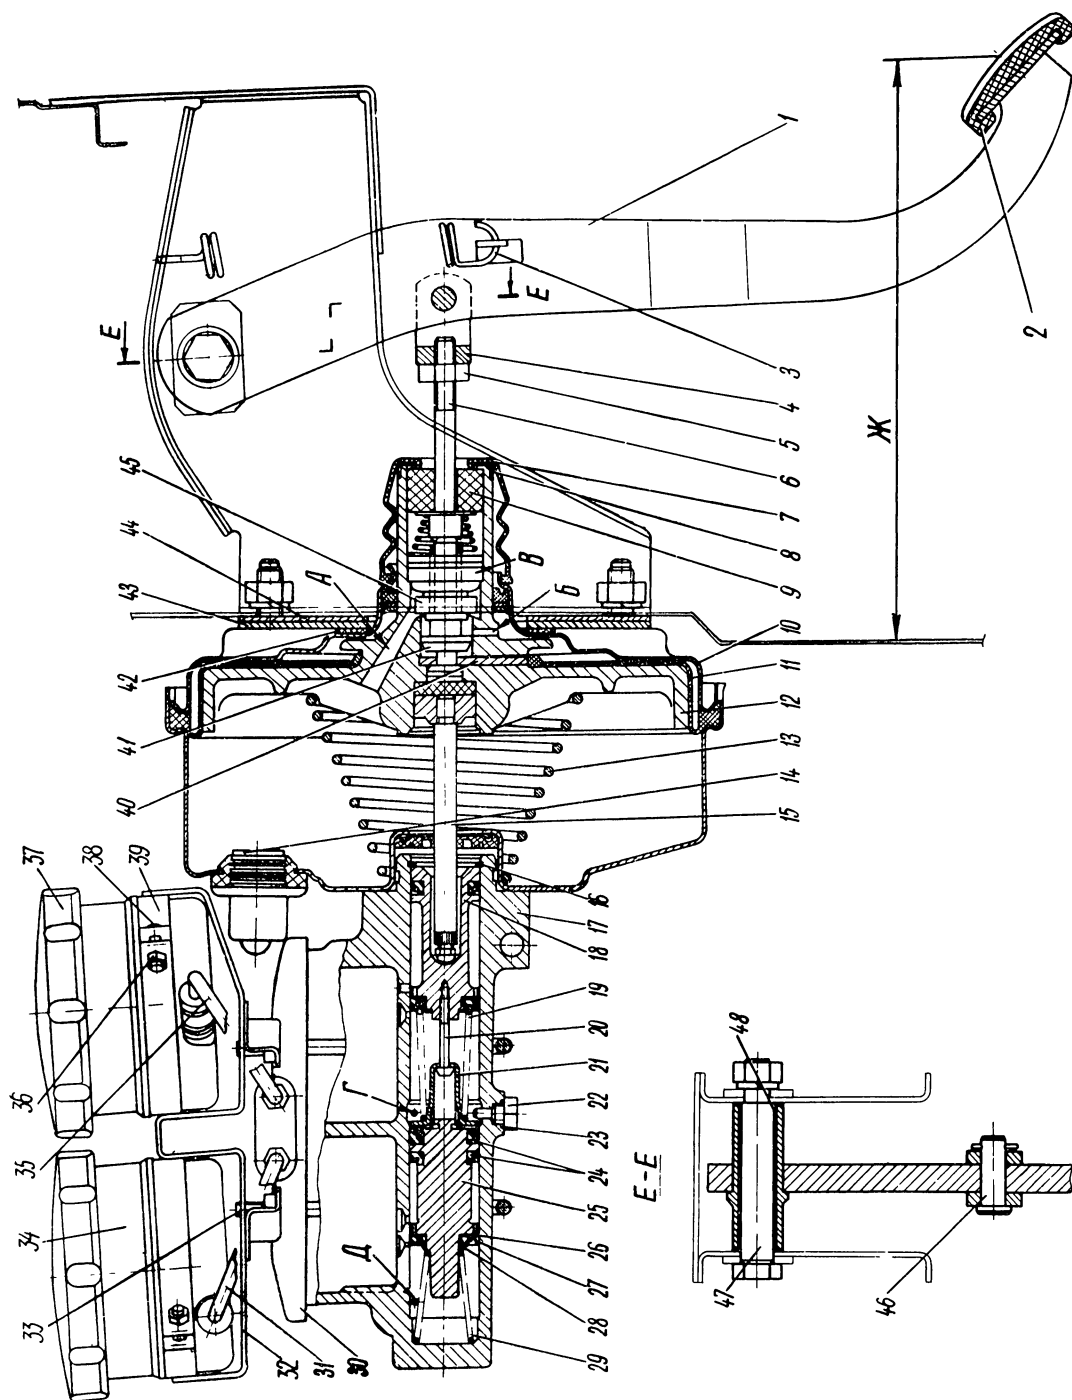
Педаль рабочих тормозов, главный цилиндр и вакуумный усилитель
